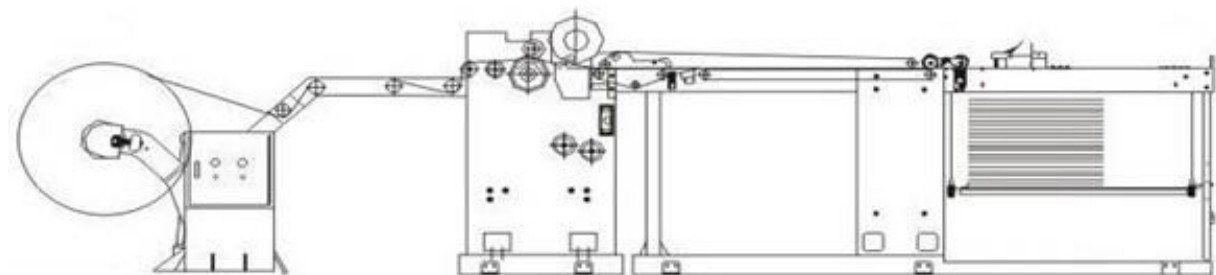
Esquematização da Máquina de Corte, adaptado de Yimu Jeta Machinery (n.d.)
